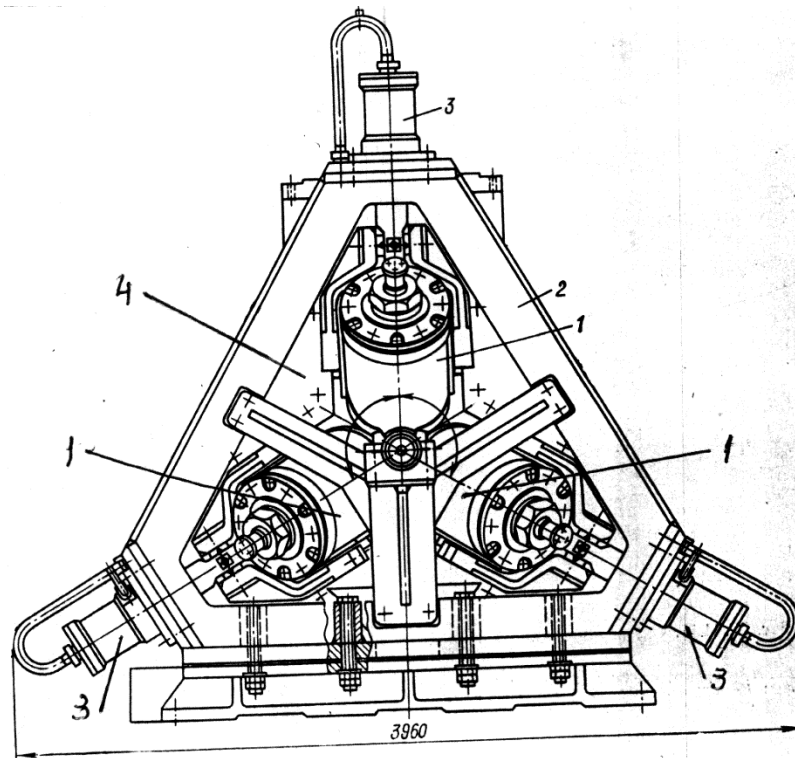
Робоча кліть тривалкового стана (вид зі сторони задачі заготовки в валки; позиції пояснені в тексті)
